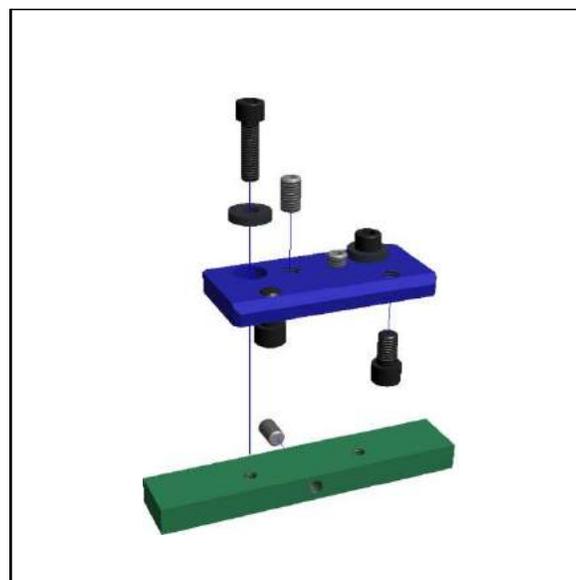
FIXATION DE LA PLAQUE DE SOUDURE PAR POINTS
